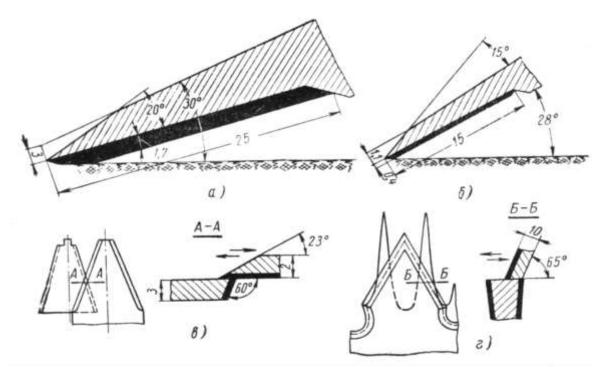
Конструкции и характер упрочнения режущих деталей а) — лемех плуга; б) — лапа культиватора; в) — сегмент и противорежущая пластина сегменто-пальцевого режущего аппарата; г) — нож и гребенка машинки для стрижки овец.
